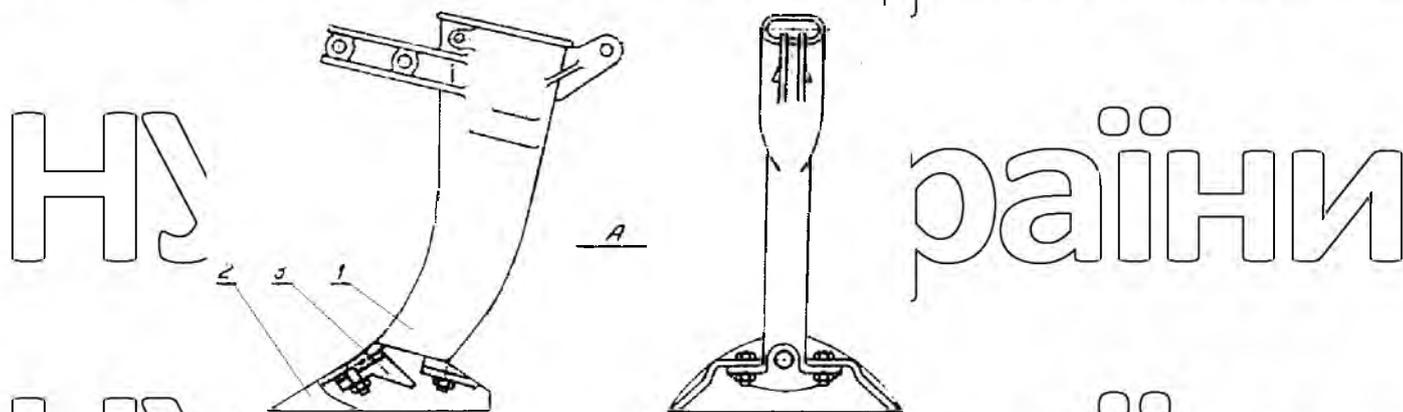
Сошник для безрядкового посіву Г.А. Гірського 1 – корпус-стійок; 2 – лапа; 3 – відсіювач.
